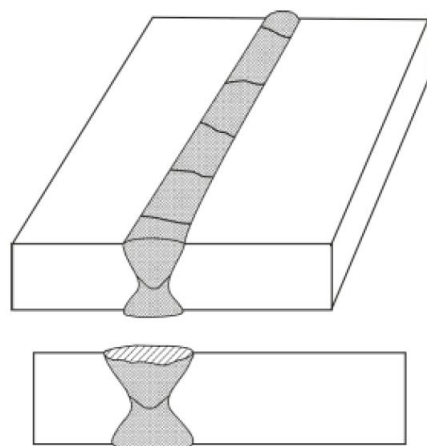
Desenho esquemático do TTS de uma solda com dureza elevada [36].
